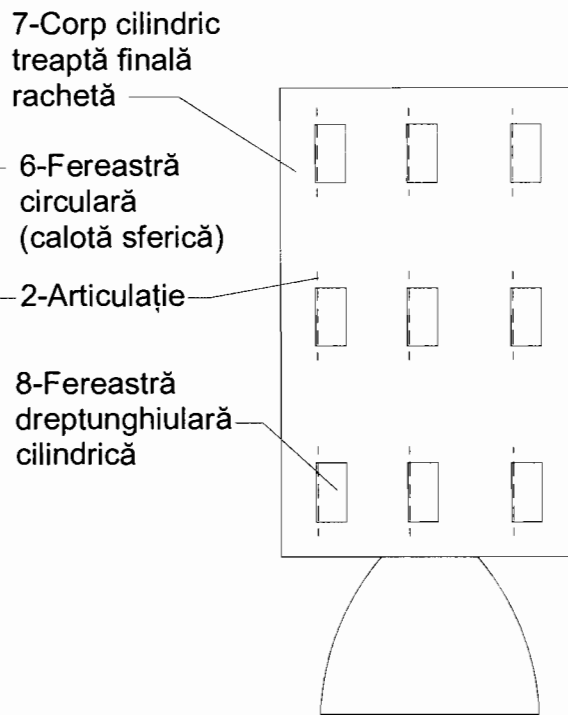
Treapta finală de rachetă lansatoare cu ferestre dreptunghiulare
